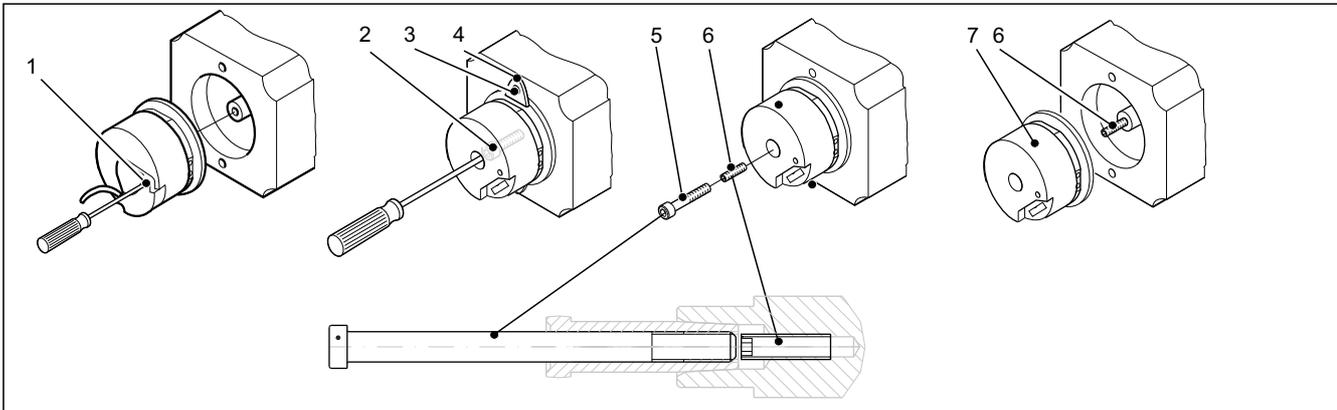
Abdrücken des Gebers mit Gewindestift und Schraube oder Sonderschraube
